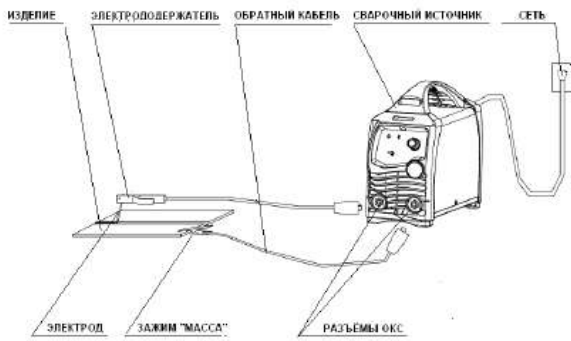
Схем подключения оборудования для ММА сварки
